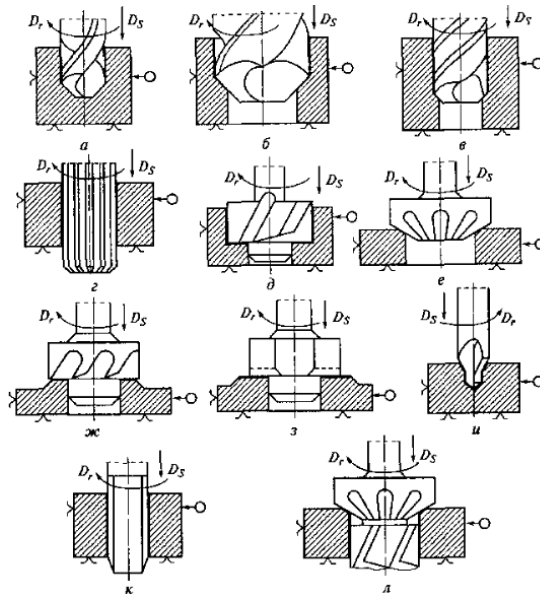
Інструменти та схеми обробки отворів на свердлильних верстатах
